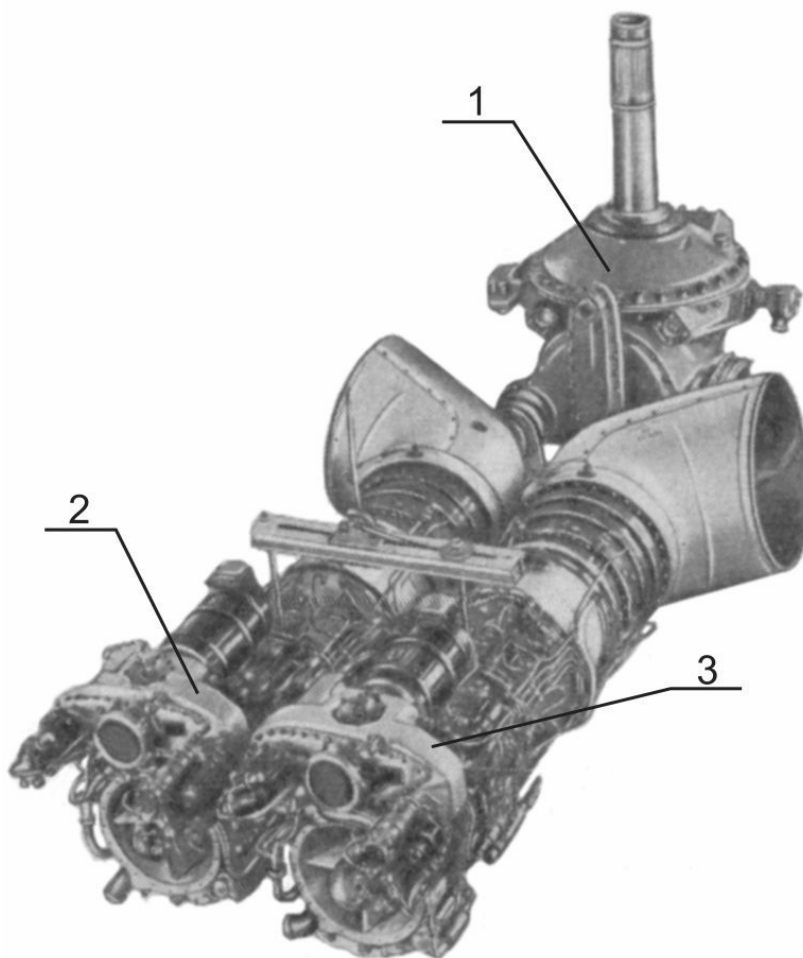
Главный редуктор и двигатели силовой установки вертолета:
